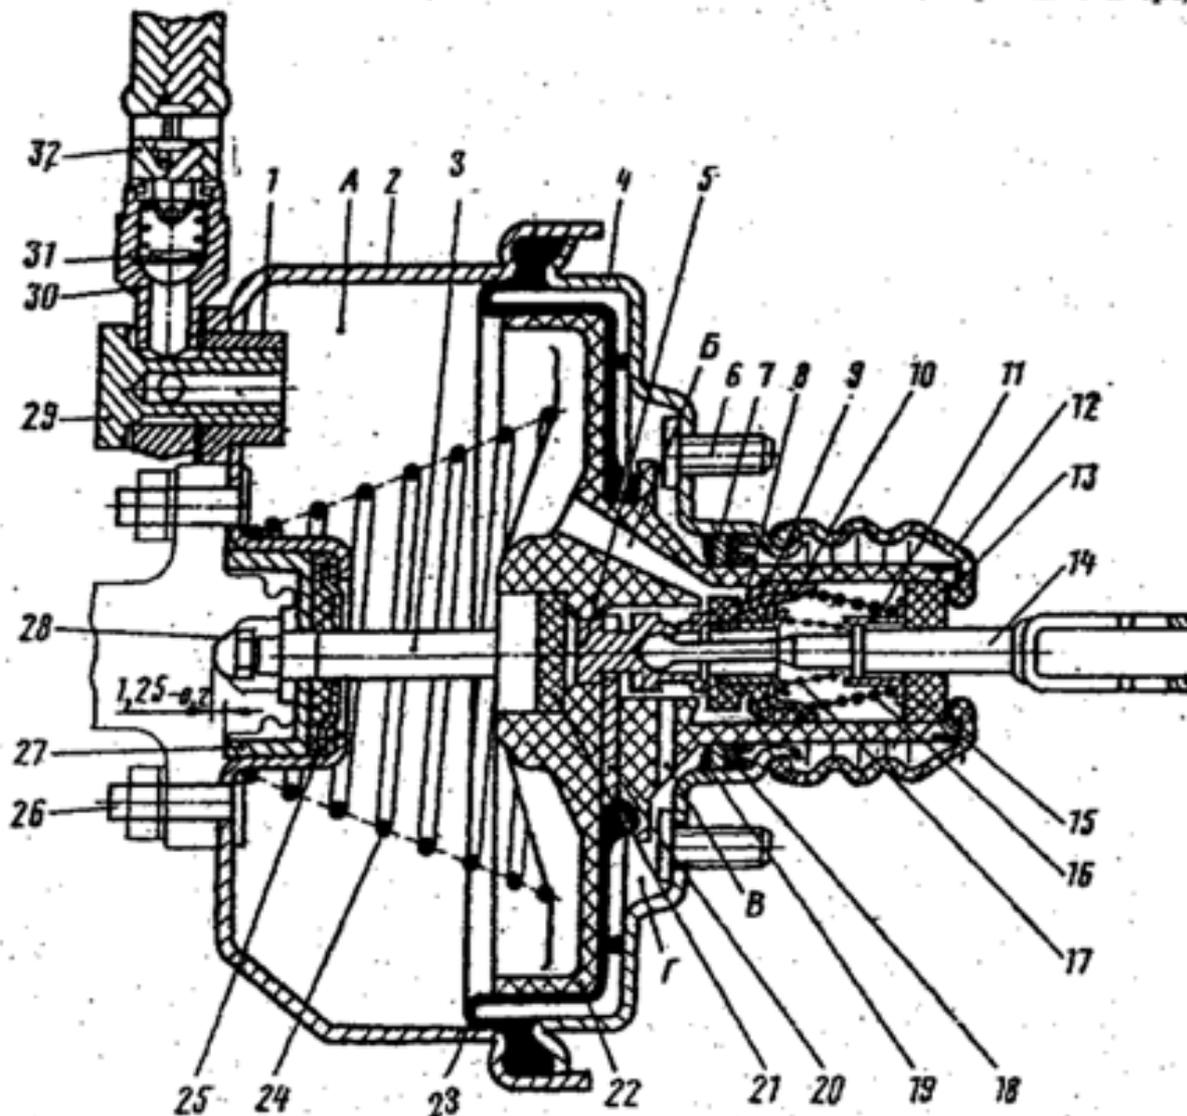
Вакуумный усилитель тормозов: 1 - втулка штуцера вакуумного шланга; 2 - корпус усилителя; 3 - шток; 4 - крышка; 5 - поршень; 6 - болт крепления усилителя; 7 - дистанционное кольцо; 8 - опорная чашка пружины клапана; 9 - клапан; 10 - опорная чашка клапана; 11 - опорная чашка возвратной пружины; 12 - защитный колпачок; 13 - обойма защитного колпачка; 14 - толкатель; 15 - воздушный фильтр; 16 - возвратная пружина клапана; 17 - пружина клапана; 18 - уплотнитель крышки корпуса; 19 - стопорное кольцо уплотнителя; 20 - упорная пластина; 21 - буфер; 22 - корпус клапана; 23 - диафрагма; 24 - возвратная пружина корпуса клапана; 25 - уплотнитель штока; 26 - болт крепления главного цилиндра; 27 - обойма уплотнителя штока; 28 - регулировочный болт; 29 - штуцер; 30 - наконечник шланга; 31 - клапан; 32 - шланг; А - вакуумная полость; Б - канал, соединяющий вакуумную полость с внутренней полостью клапана; В - канал, соединяющий внутреннюю полость клапана с атмосферной полостью; Г - атмосферная полость.
